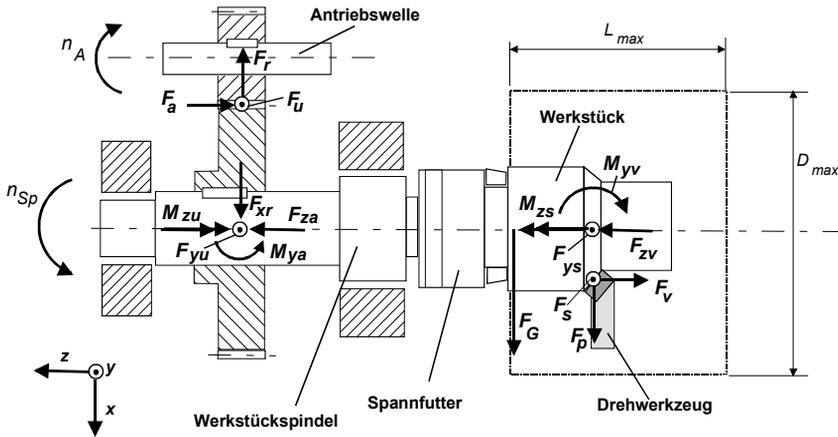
Kräfte und Momente an der Werkstückspindel bei einer Drehmaschine
